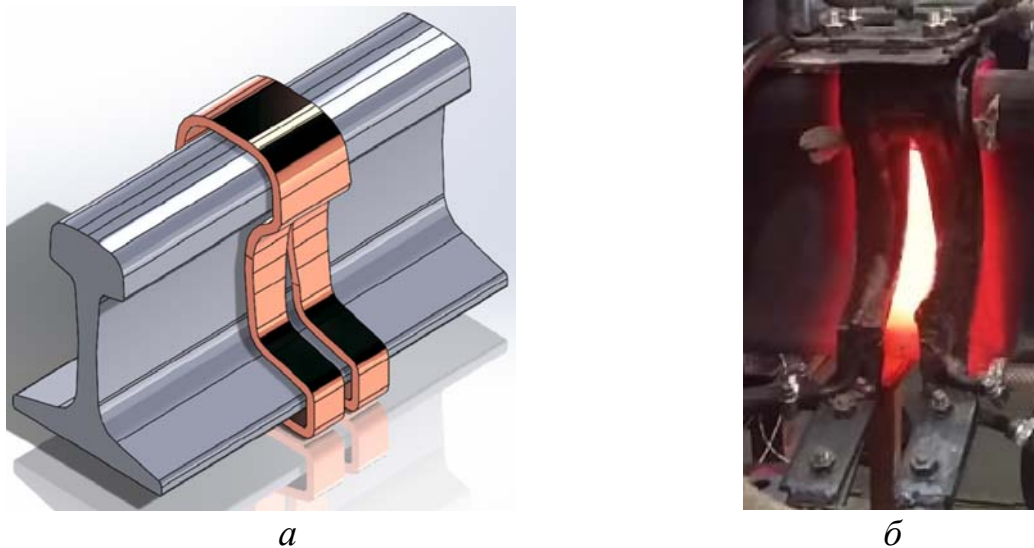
Розроблена конструкція частково розщепленого індуктора – *а* і процес об'ємної ТО індуктором зварного з'єднання залізничної рейки типу Р65 – *б*.
